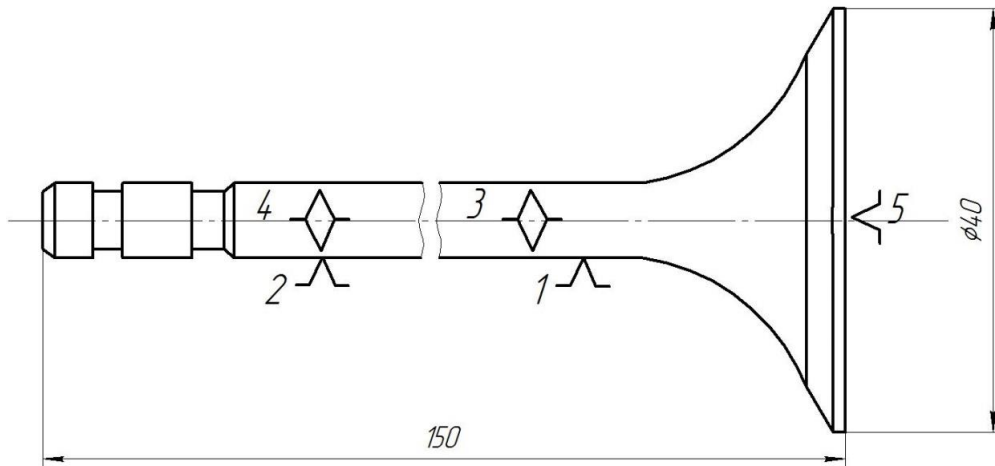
Ескіз впускного клапана метод базування при обробці токарній
